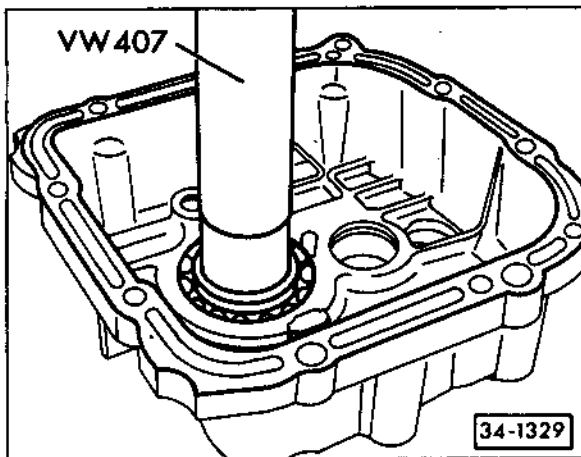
Rillenkugellager aus Lagerschild auspressen
